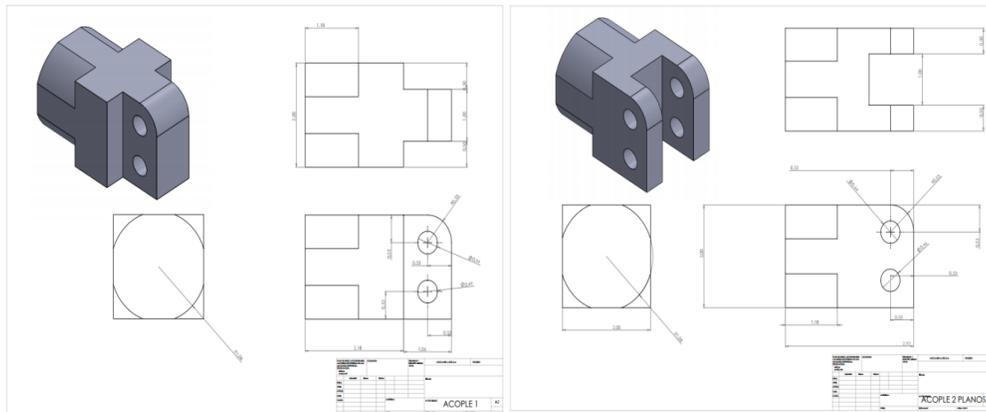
Planos para construcción de piezas necesarias. Fuente: autor
